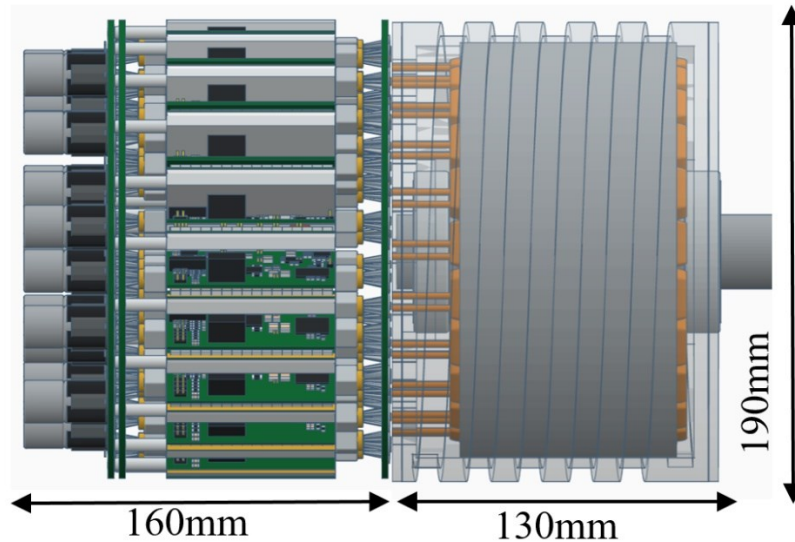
Vue 3D du GMP hendécaphasé assemblé.
